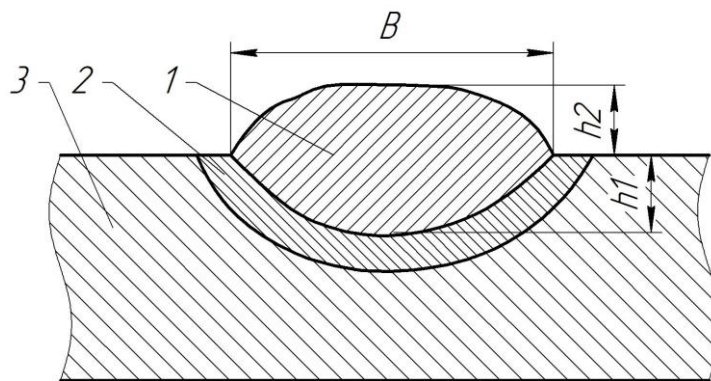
Валик звареного шва: 1 – наплавлений метал; 2 – зона термічного впливу; 3 – основний метал; B – ширина валика
